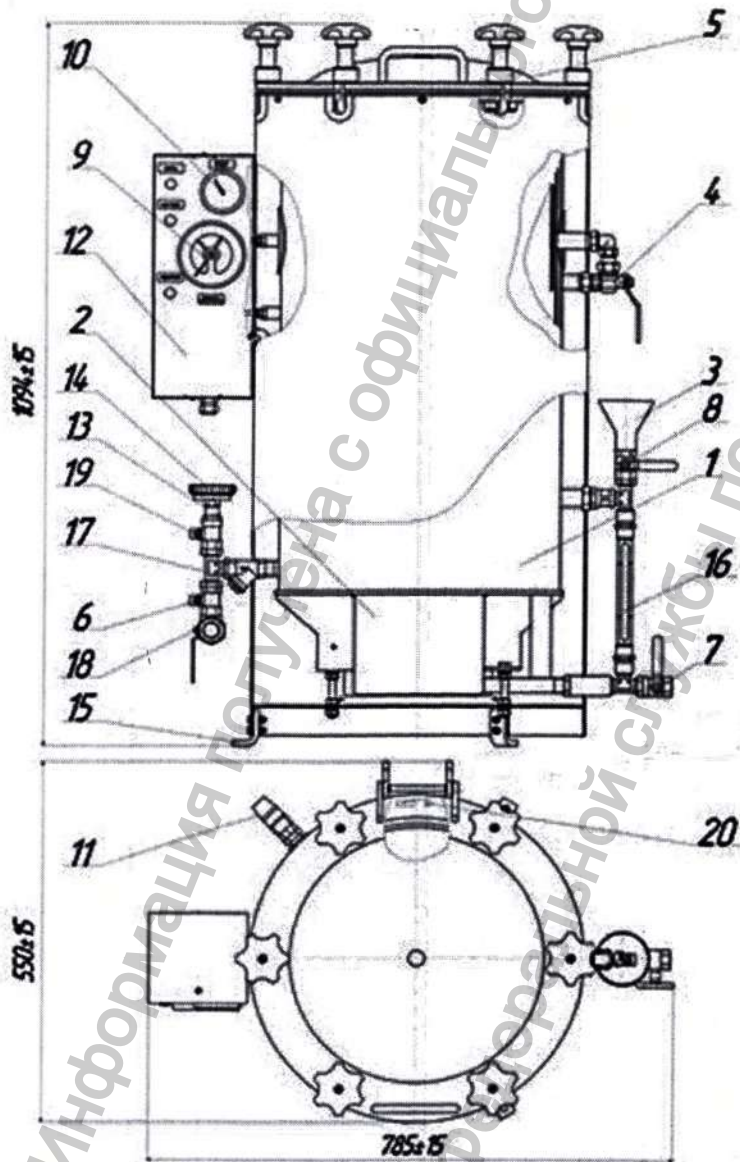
Стерилизатор паровой ВКа-75-ПЗ:
